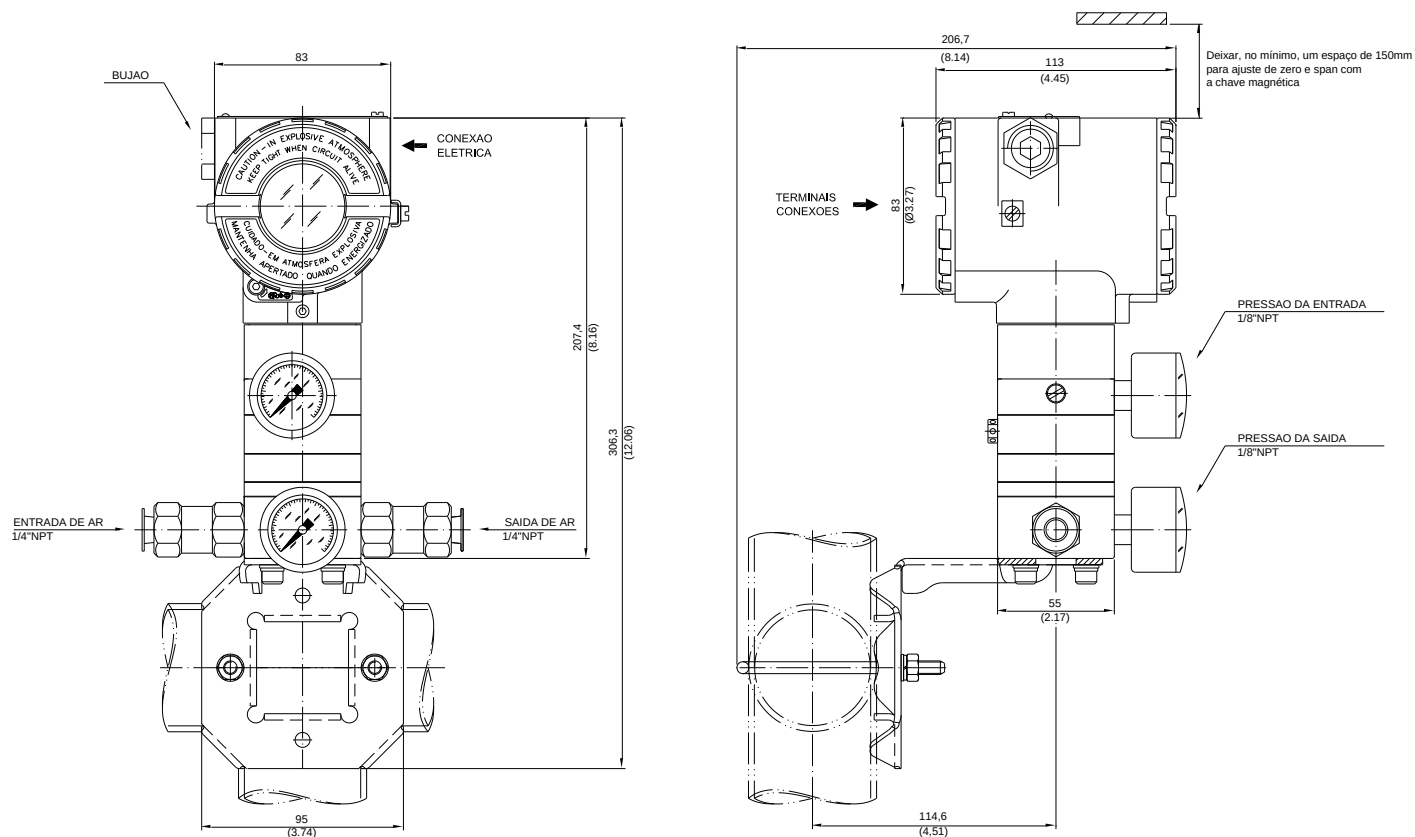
Desenho Dimensional e Posição de Montagem do Conversor
